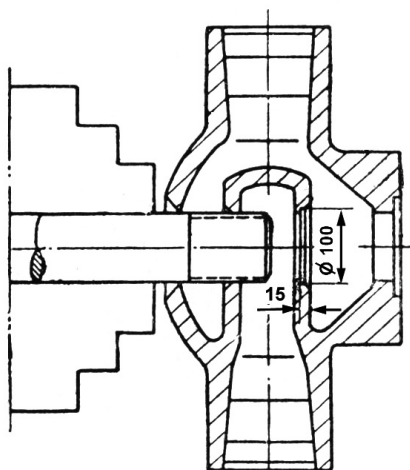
Установка корпуса клапана для расточки под стакан
